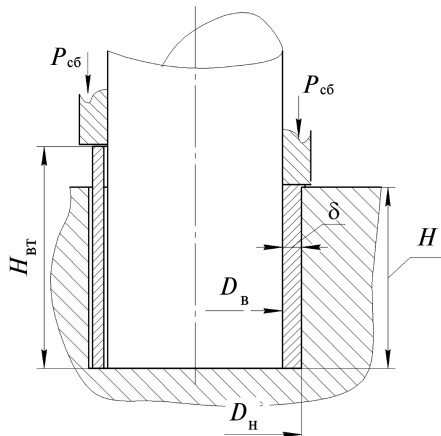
Схема сборки прессового соединения с промежуточной втулкой
